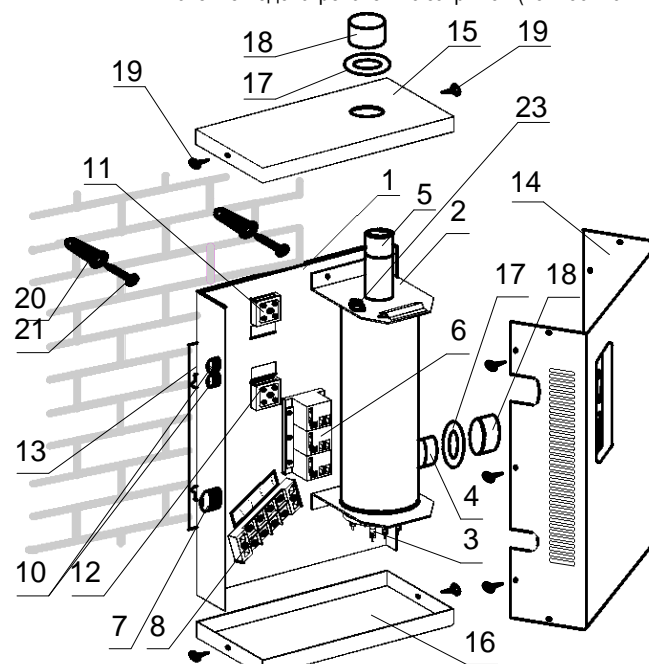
Конструкция электроводонагревателя и способ крепления его к стене
